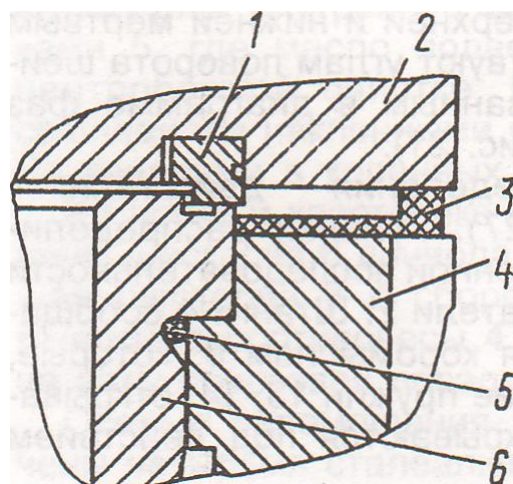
Стыки головки цилиндра и гильзы, головки и блока цилиндров: 1- кольцо стопорное; 2 - головка цилиндра; 3 - прокладка; 4-блок цилиндров; 5 - кольцо уплотнительное гильзы; 6- гильза цилиндров.
